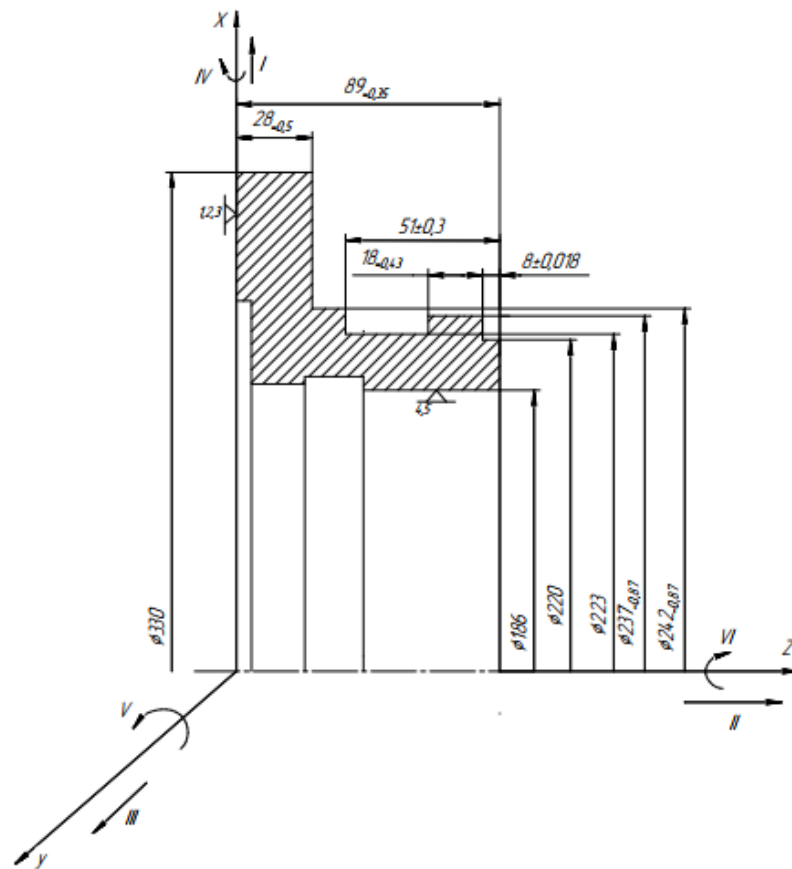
Схема базування заготовки по діаметру 186 мм і прилеглому торцю $28_{-0,5}$ мм
